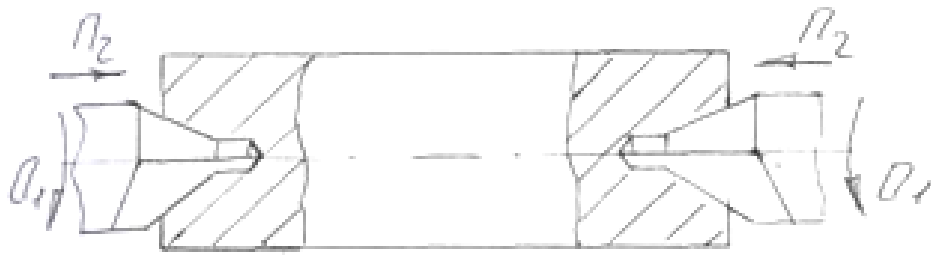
Схема обробки центрувальними свердлами з нерухомою заготовкою
